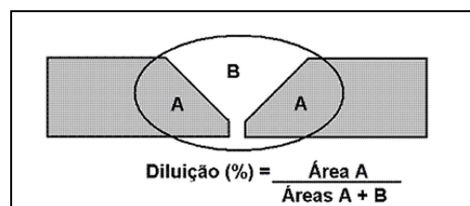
Desenho esquemático da diluição em uma junta soldada (Adaptado de UFTPR, 2006).
